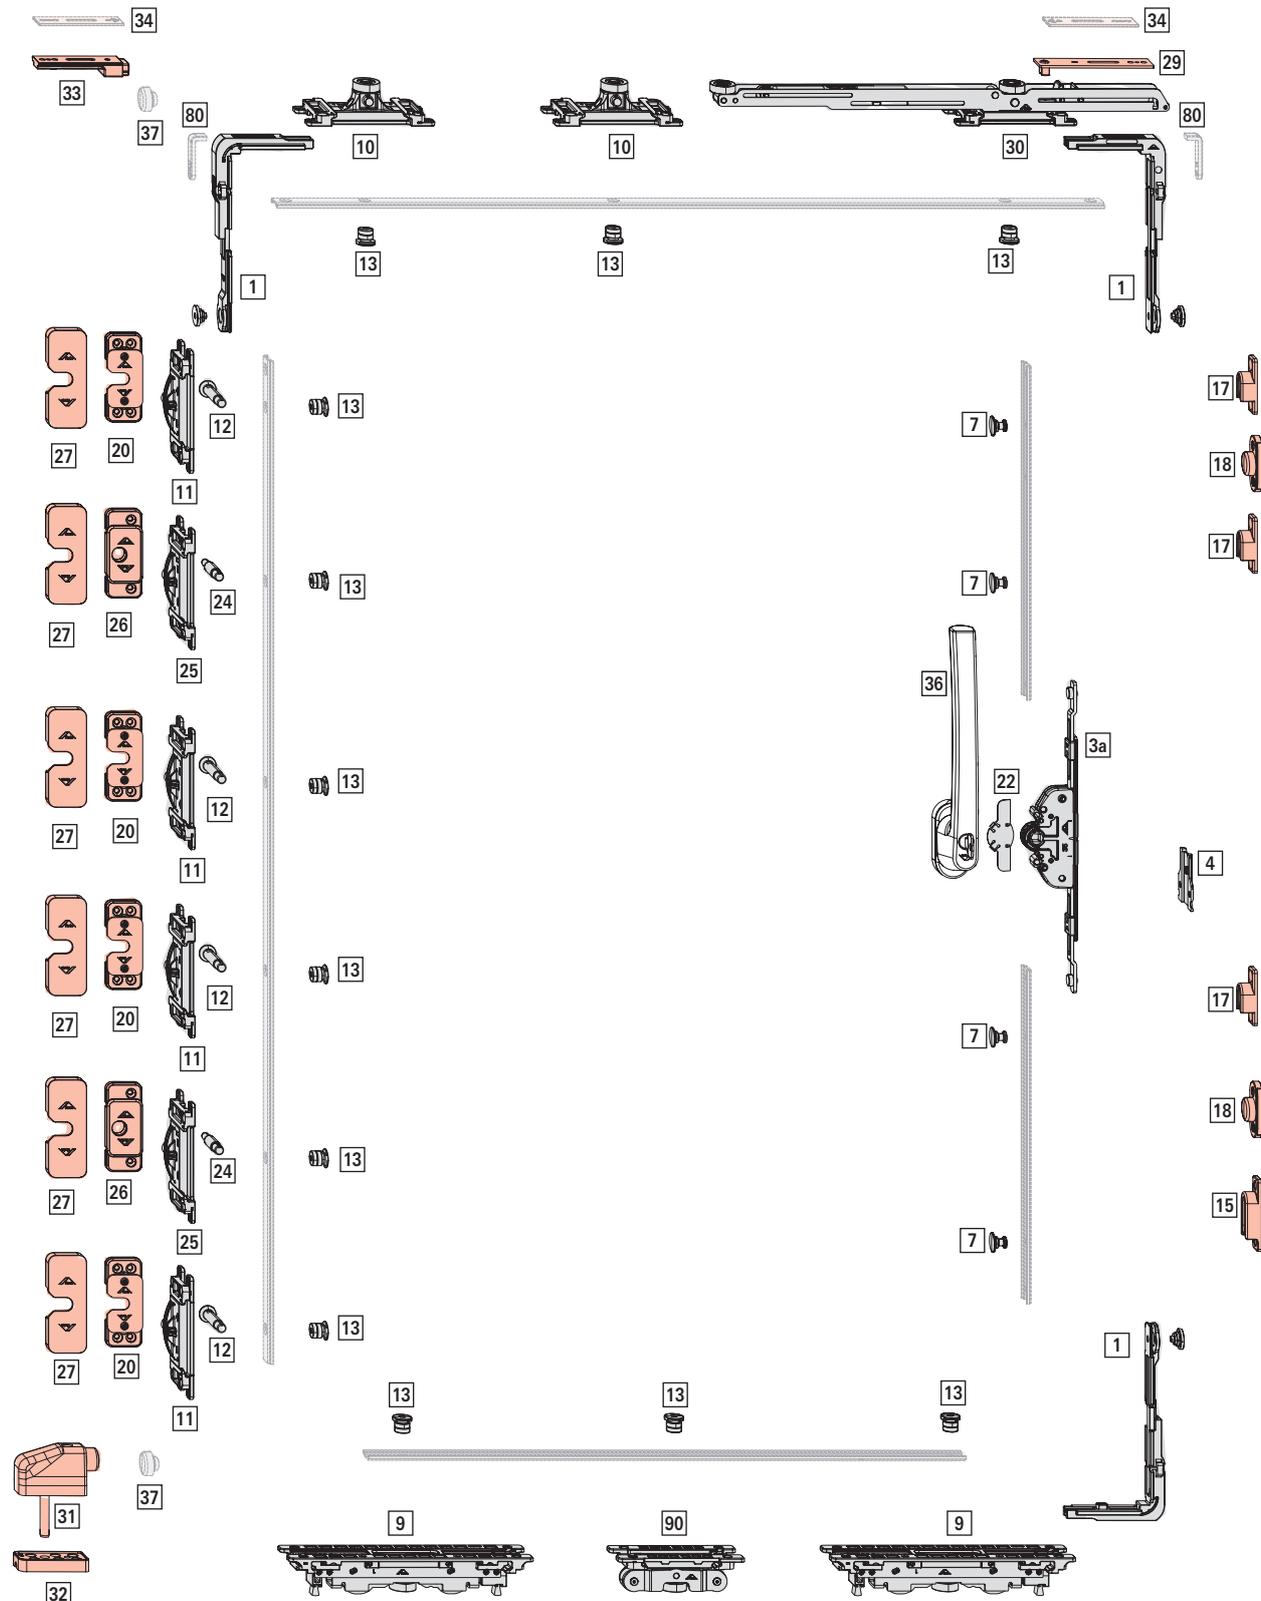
abgebildet: Ausführung DIN L; FB 1500 mm; FH 2500 mm; Getriebe DM 35; RC 2
